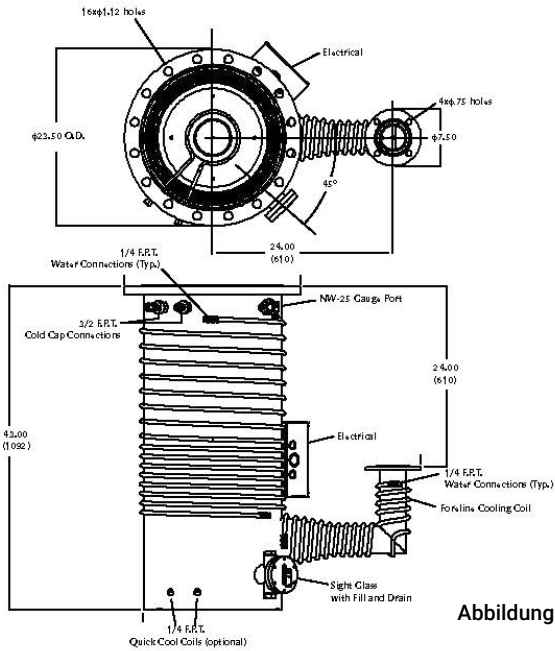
HS-16 Grundriss mit ASA-Flanschen
